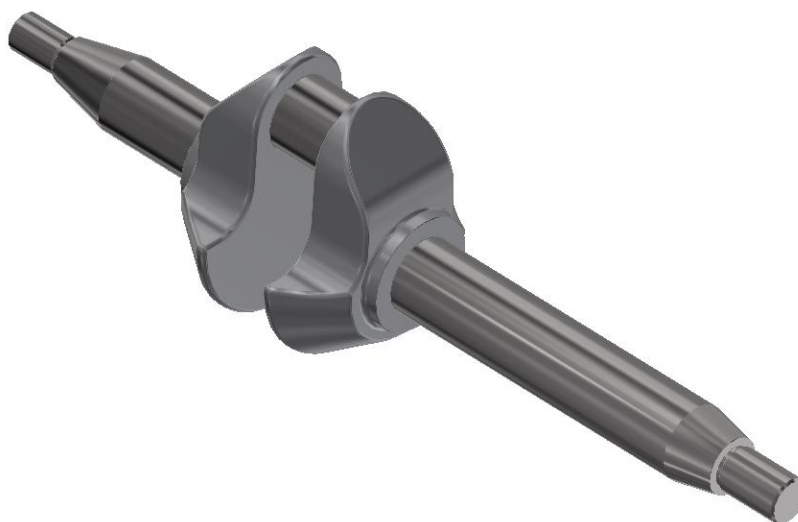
Provedení ojničního ložiska u motoru Lawn-Boy V [1]
